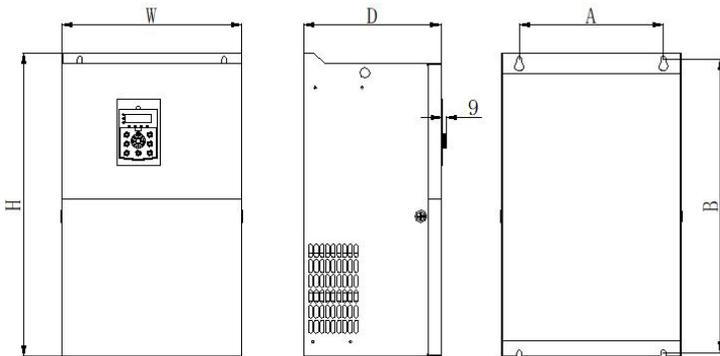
380V (4T) 18.5~132kW 变频器外形尺寸及安装尺寸示意图
